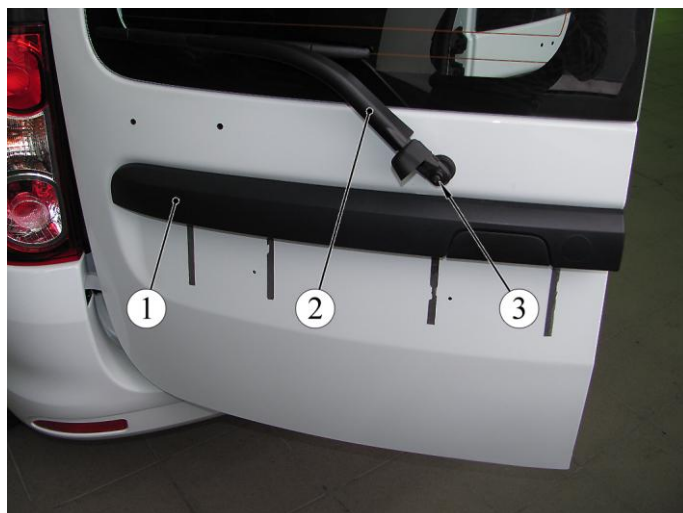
Крепление рычага стеклоочистителя:
